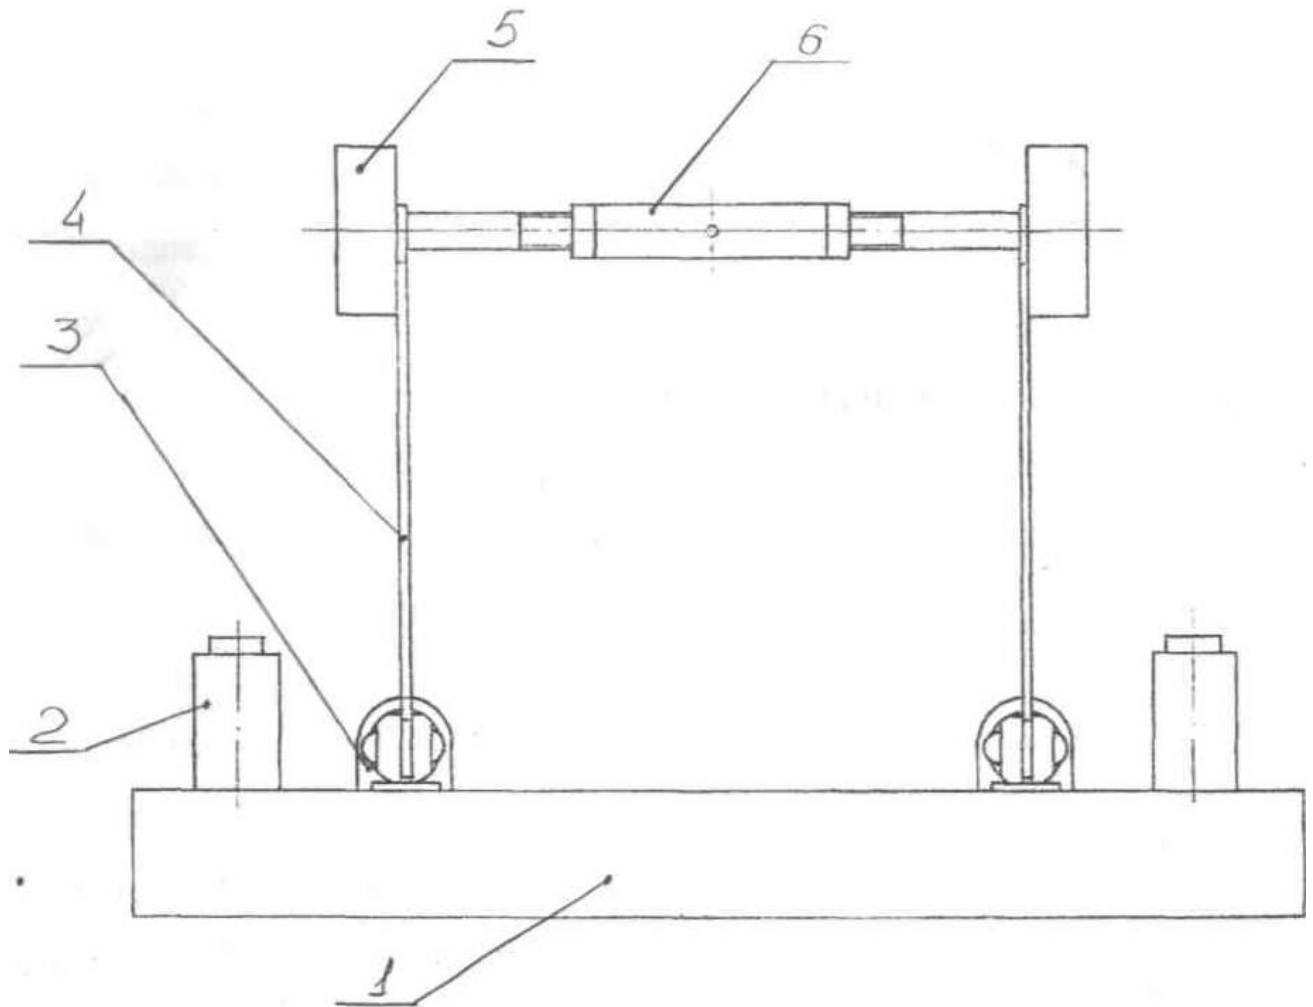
Схема обладнання для визначення технічного стану ресорної підвіски:
